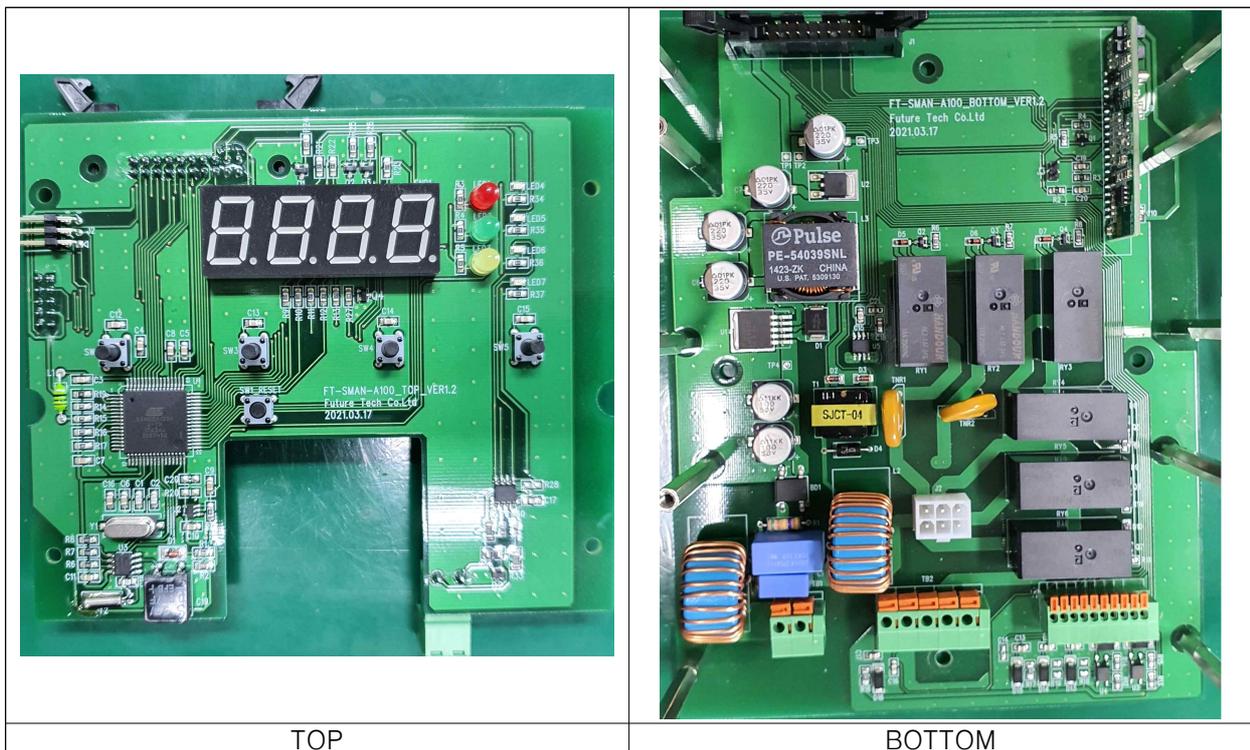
은 스마트 구동기 노드의 PCB Artwork이다.
